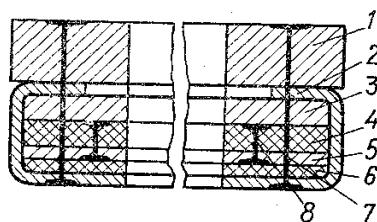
Нагревательный элемент пневматического пресса для приклеивания деки и дна:
